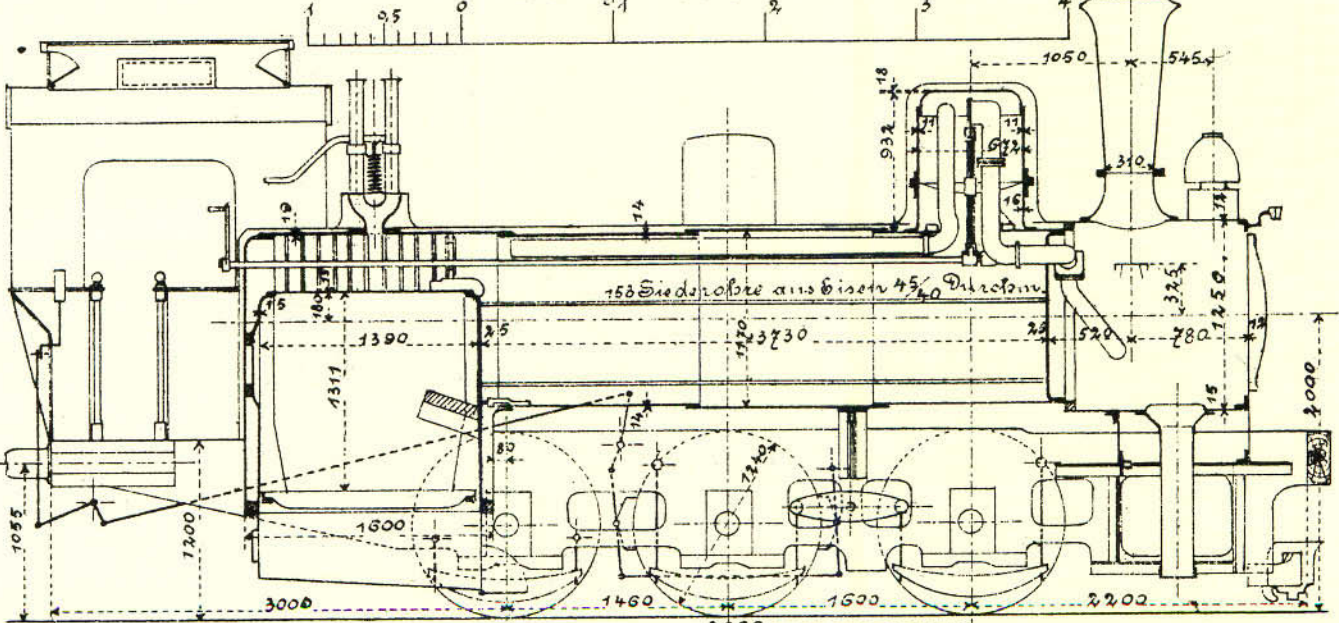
1:50-Zeichnung der VT der dritten Bauform.
